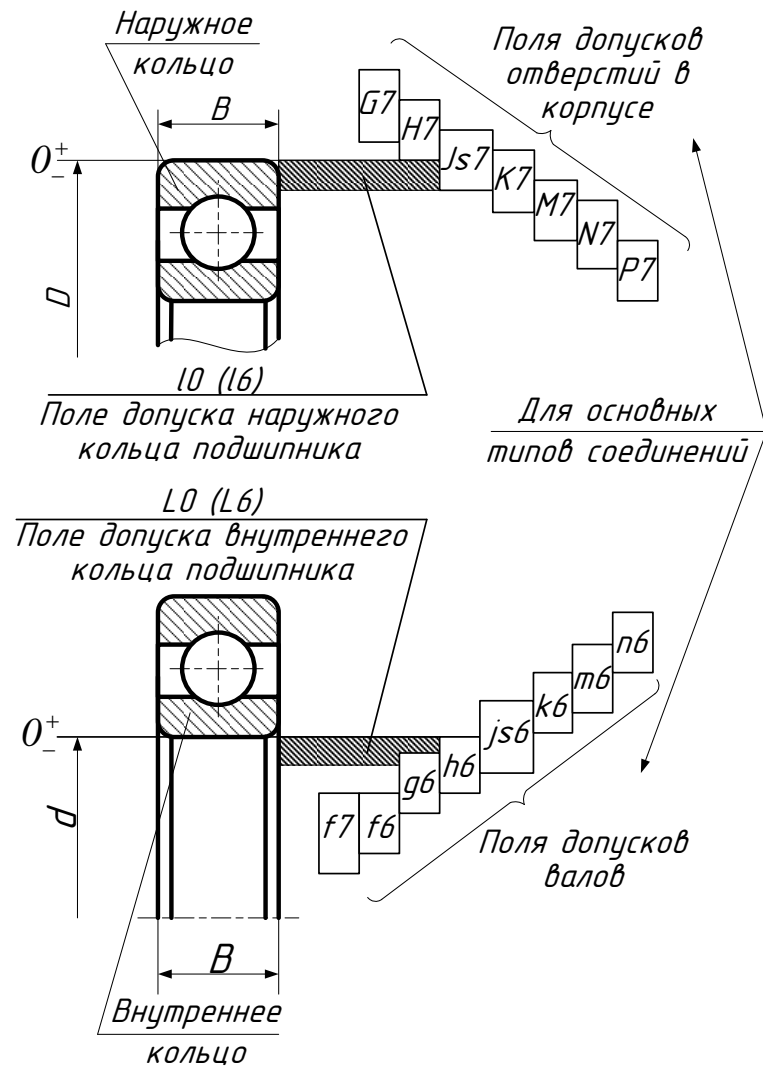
Поля допусков посадочных поверхностей подшипников, отверстий и валов для установки подшипников качения 0 и 6 классов точности
